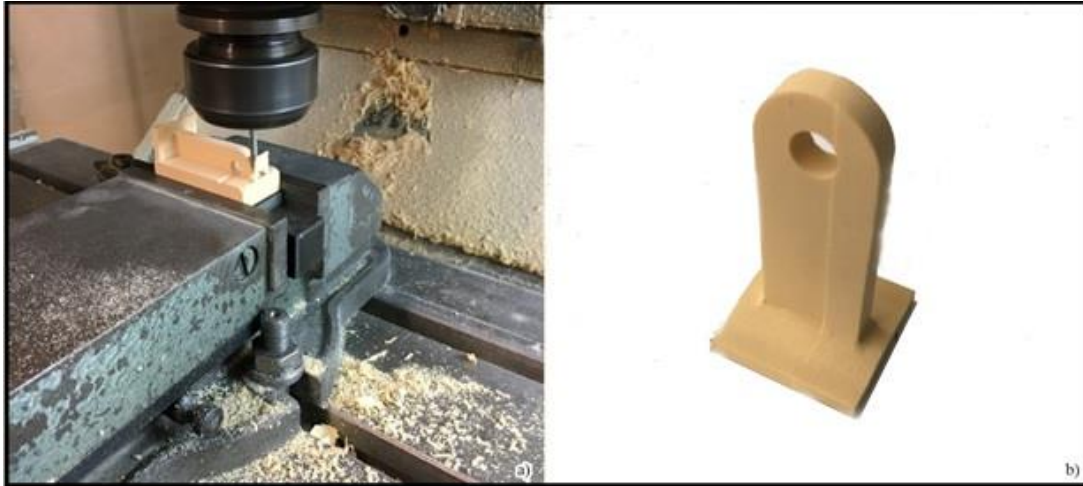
Processo de Maquinagem: a) Execução da peça durante o segundo aperto; b) Resultado Final
